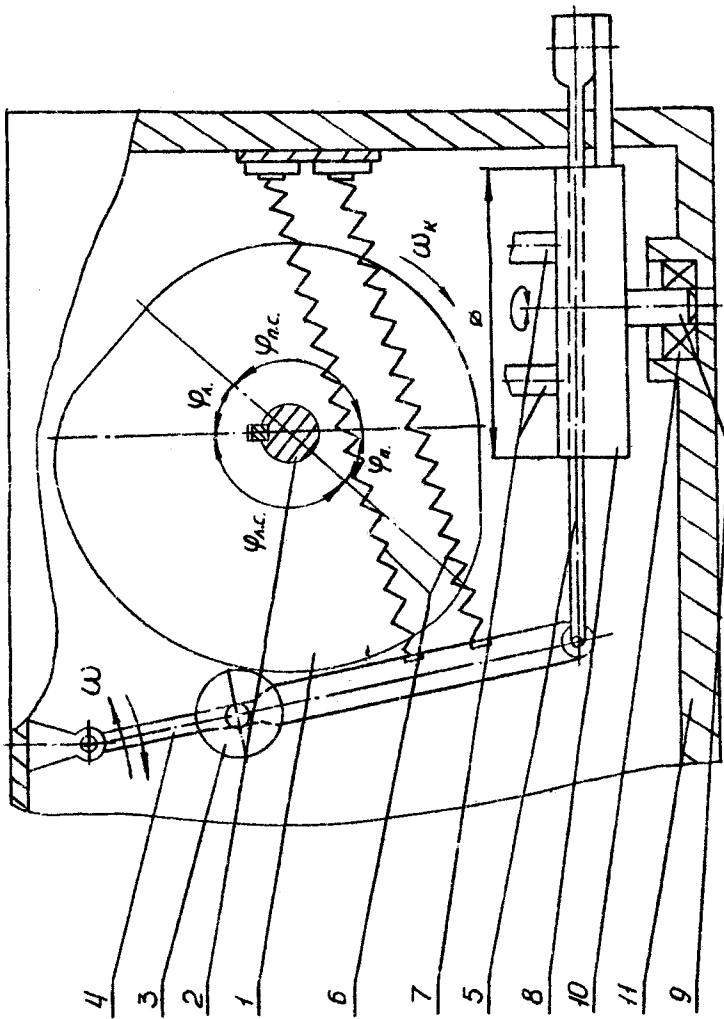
Механизм поворота руки от кулакка I, автодриватор "Бонни" IV
